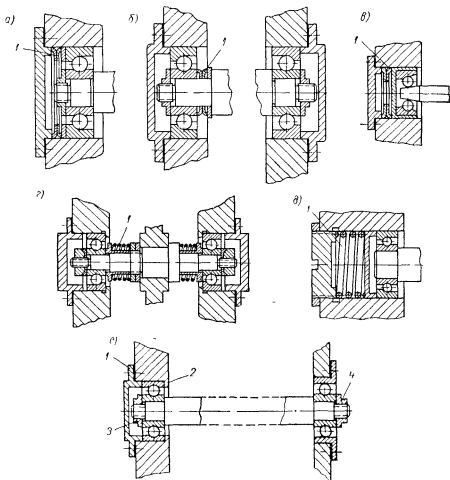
Схемы крепления подшипников с компенсирующими устройствами
